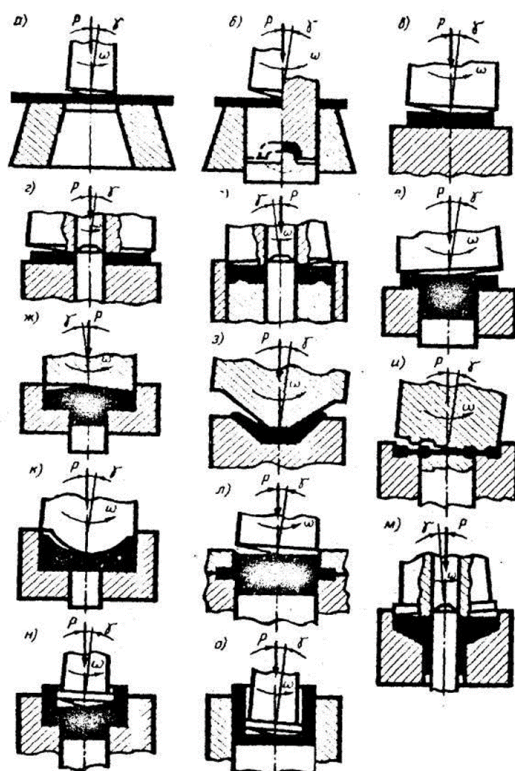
Технологические схемы формообразования изделий с применением сферодвижного механизма: а –вырубка; б – вырубка с формовкой; в – открытая осадка сплошной заготовки; г – открытая осадка кольцевой заготовки; д – закрытая осадка; е – открытая осадка фланца; ж – закрытая осадка фланца; з – полузакрытая формовка; и, к – закрытая формовка; л – поперечное выдавливание фланца; м, н, о – прямое, комбинированное и обратное выдавливание фланца.
